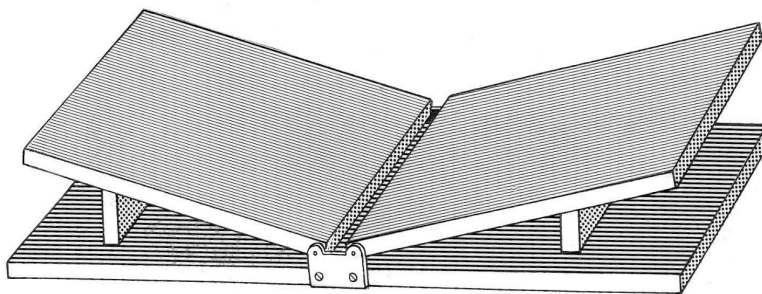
Suporte para serrar, construído de madeira rija: faia, freixo ou pinho.
